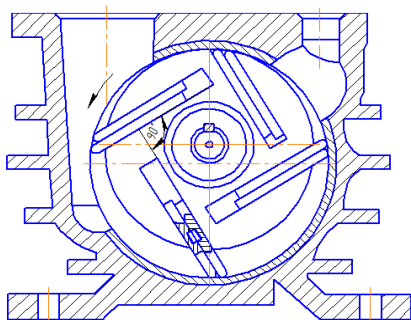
Разработанный пластинчато-роторный вакуумный насос НВУ-2,8
